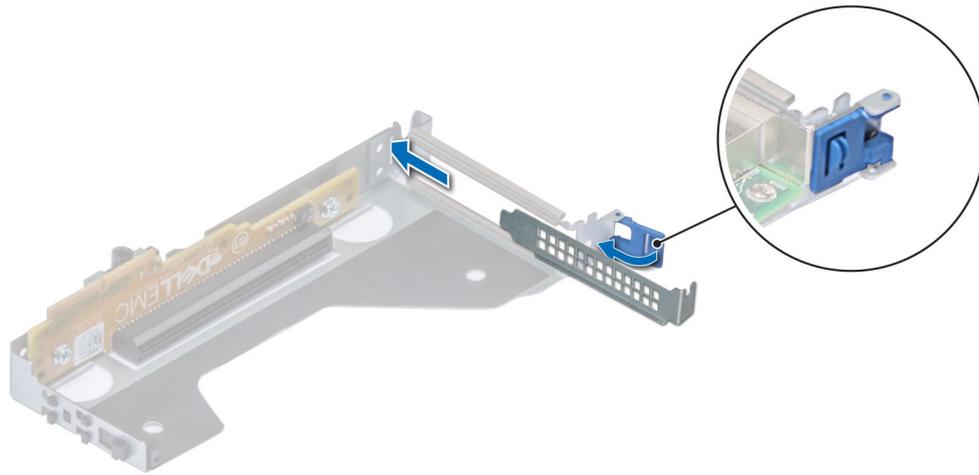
Installation d'une plaque de recouvrement pour la carte de montage mi-hauteur
